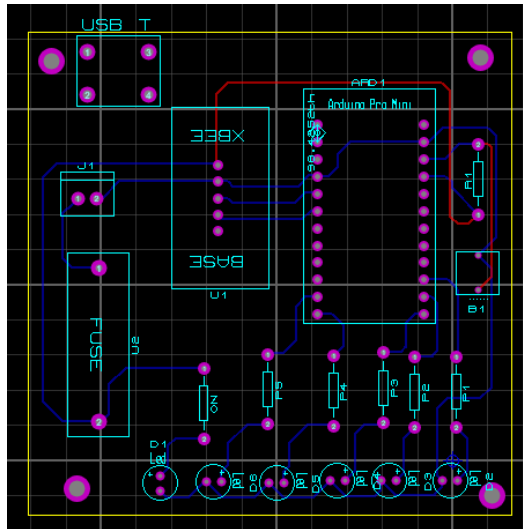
Vista del PCB Layout en Proteus de Zigbee Router
